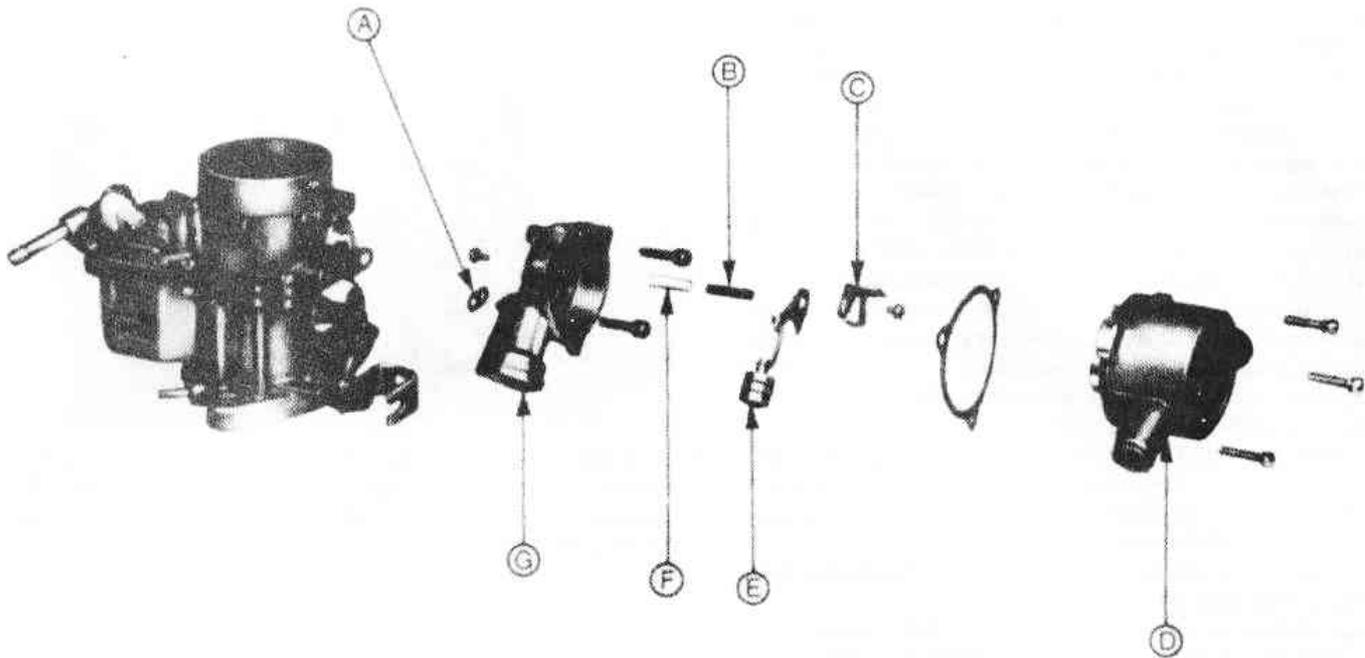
Детали автоматической воздушной заслонки карбюратора "Форд" (Разд.23)
